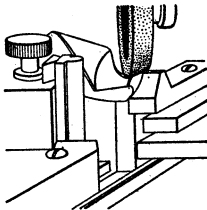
Ausspitzen eines Spiralbohrers auf der Ausspitzmaschine.
